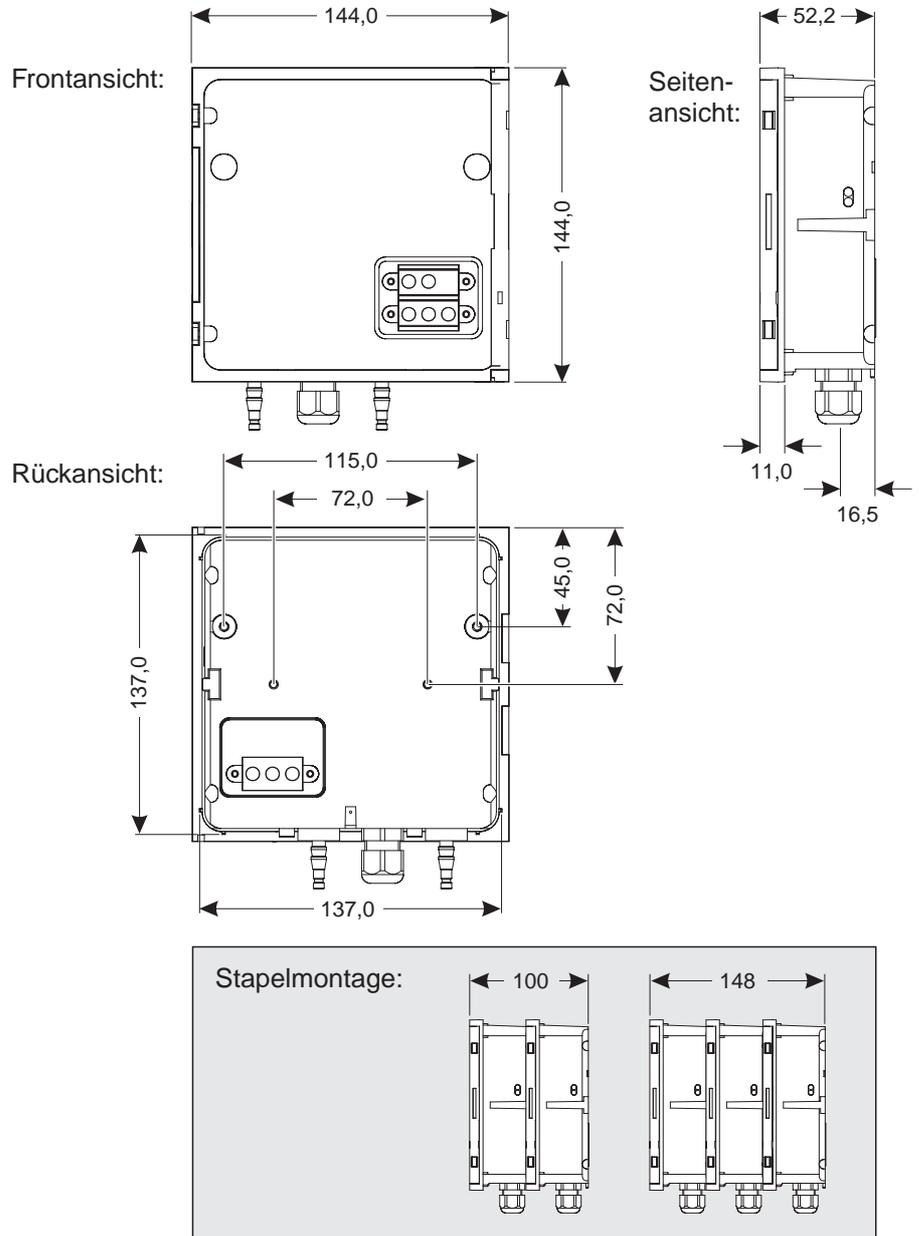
Maßzeichnung MIQ/CHV (Maße in mm)
